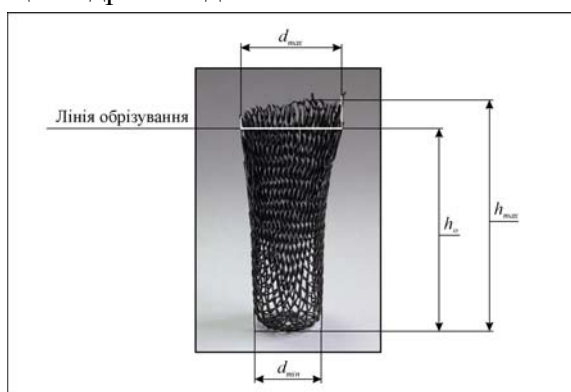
Четверте витягування циліндричної деталі із металевої сітки
